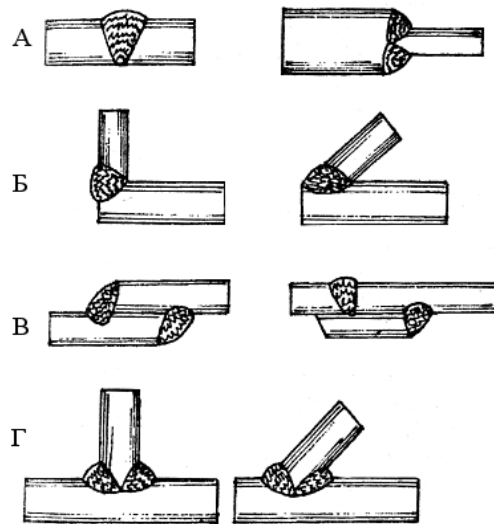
Соединения сварные: А – стыковые; Б – угловые; В-нахлесточные; Г – тавровые
